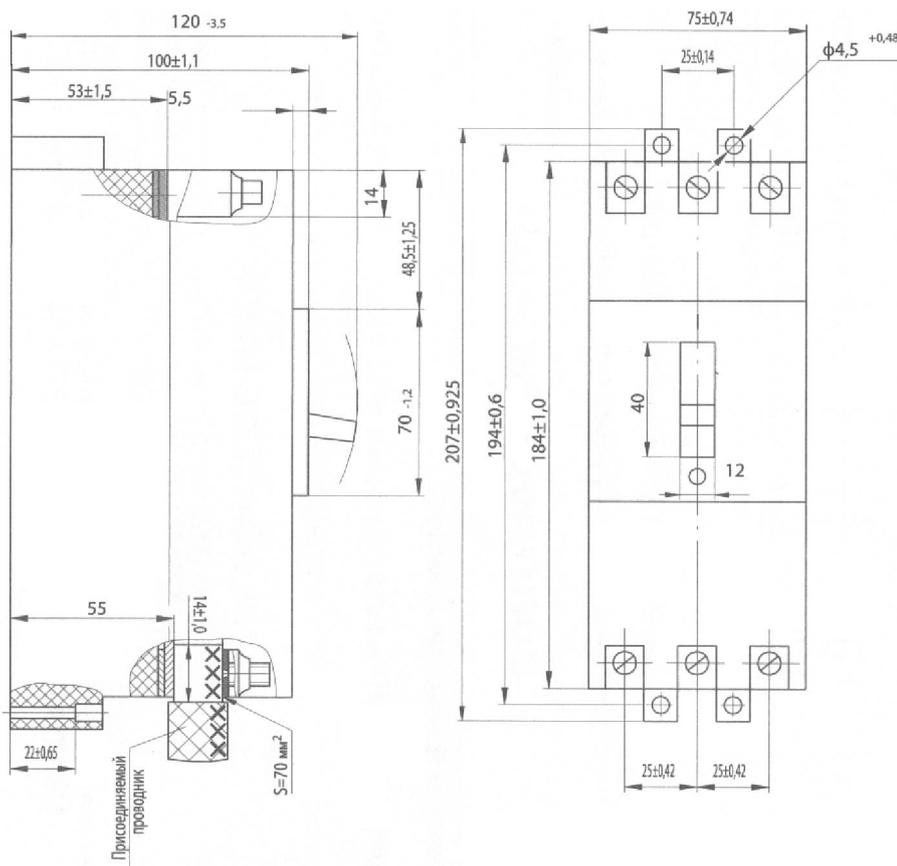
Габаритные размеры выключателя АЕ-2056
